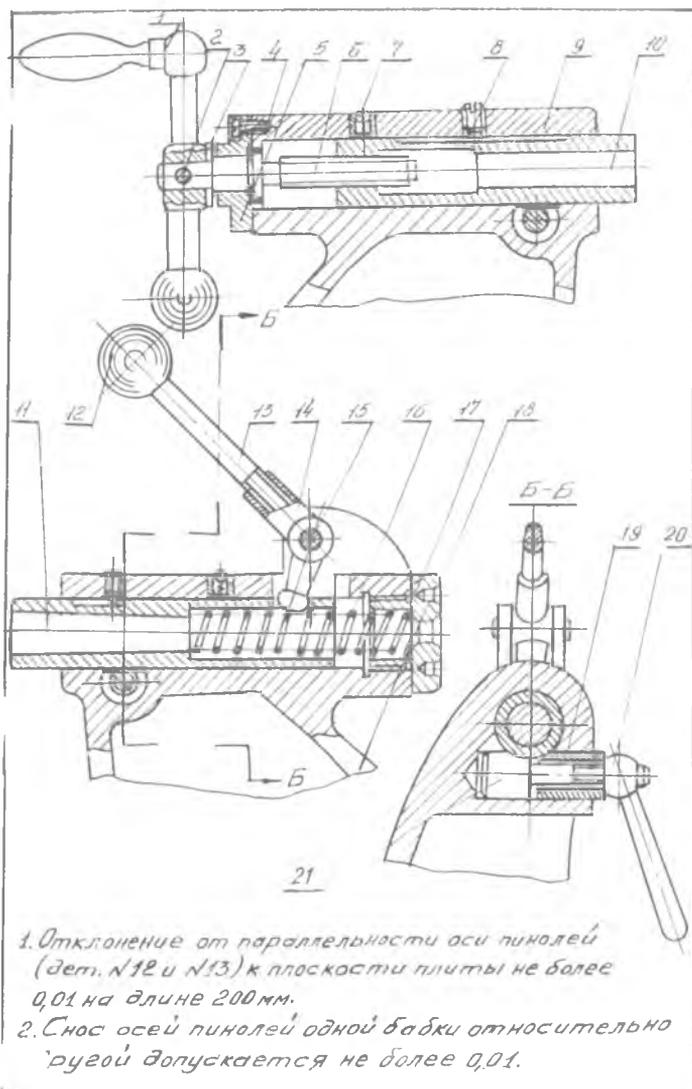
Бабки для центров с подвижной пинолью. 1, 20 — рукоятка; 2, 15 — штифт; 3 — шайба; 4, 6, 8 — винты; 5 — фланец; 7 — масленка; 9, 18 — бабки; 10, 11 — пиноли; 12 — шаровая ручка; 13 — шпилька; 14 — рычаг; 16 — пружина; 17 — заглушка; 19 — втулка; 21 — болт
